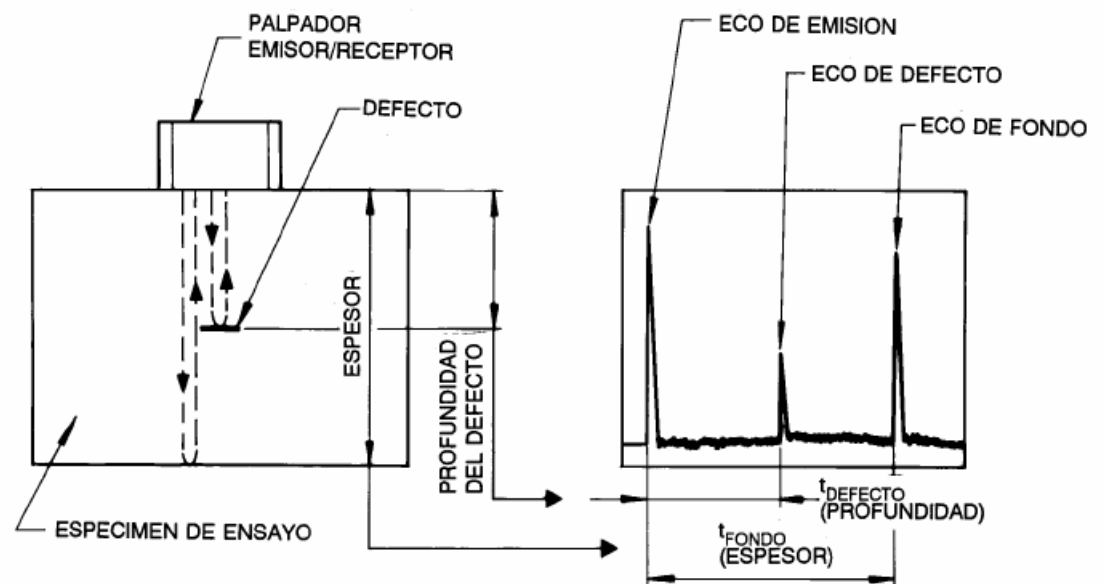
Ensayo por Pulso-eco con un solo palpador
